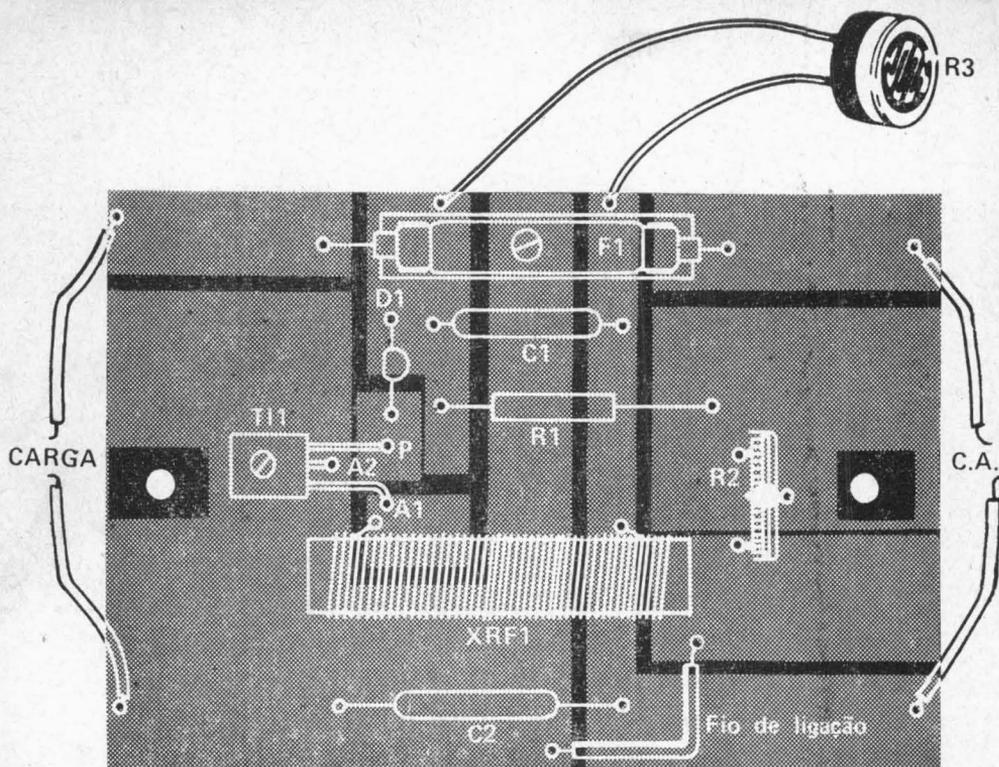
Disposição dos componentes na plaqueta da Fig. 2. O triac é fixado à face cobreada, que serve de dissipador de calor.
